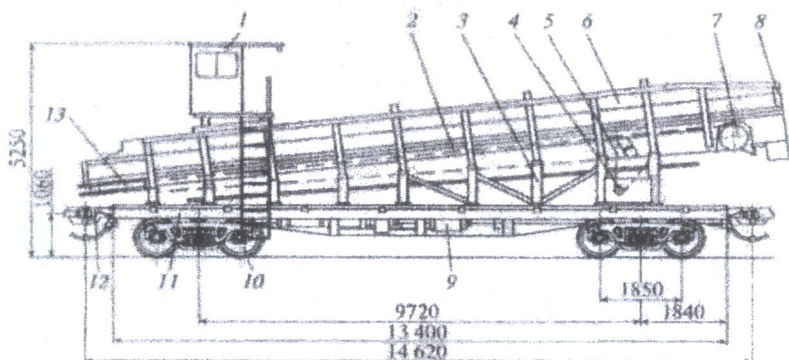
Универсальный полувагон: 1- кабина управления; 2 - ленточный конвейер-накопитель; 3 - рама; 4 - привод конвейера; 5 - цепная передача; 6 - продольный борт кузова; 7 - приводной барабан конвейера; 8 - задний борт; 9 - тормозное оборудование; 10 - ходовая тележка типа 18-100; 11 - рама платформы; 12 - автосцепка; 13 - натяжной барабан
